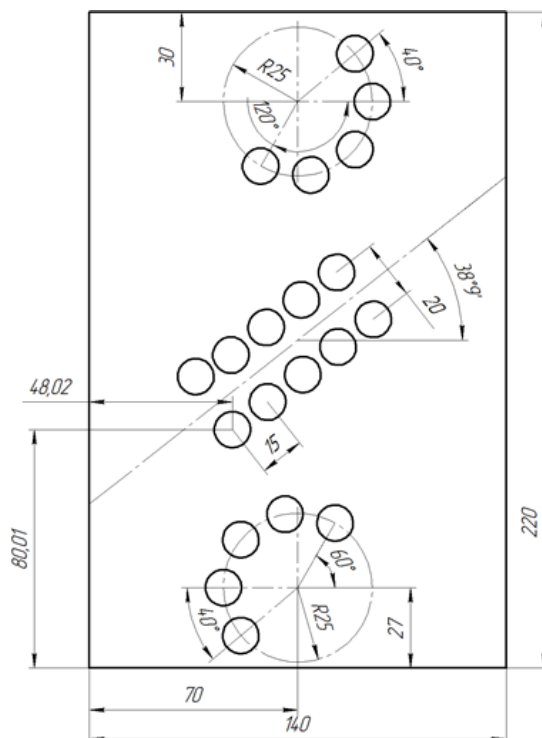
Чертеж детали, сделанный в САПР КОМПАС-2D
